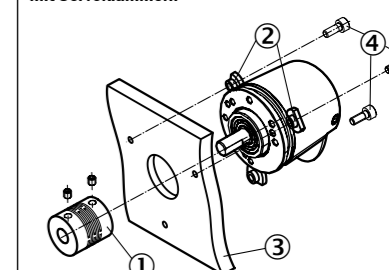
Anbau DBS50 Klemmflansch über flanschseitige Gewindebohrungen
